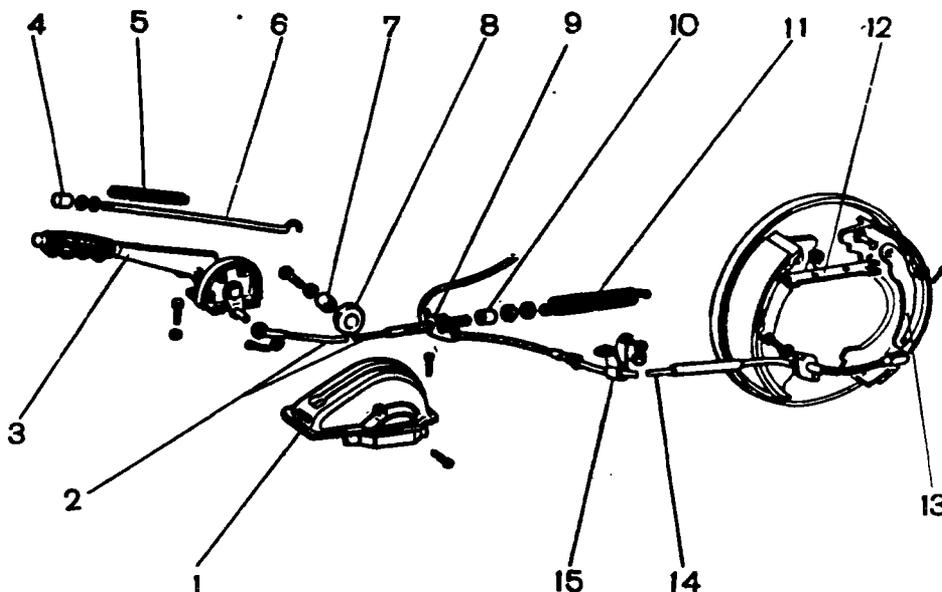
Детали привода стояночного тормоза: 1 - чехол; 2 - передний трос; 3 - рычаг; 4 - кнопка; 5 - пружина тяги; 6 - тяга защелки; 7 - втулка; 8 - ролик; 9 - направляющая заднего троса; 10 - распорная втулка; 11 - оттяжная пружина; 12 - распорная планка; 13 - рычаг ручного привода колодок; 14 - задний трос; 15 - кронштейн крепления заднего троса
